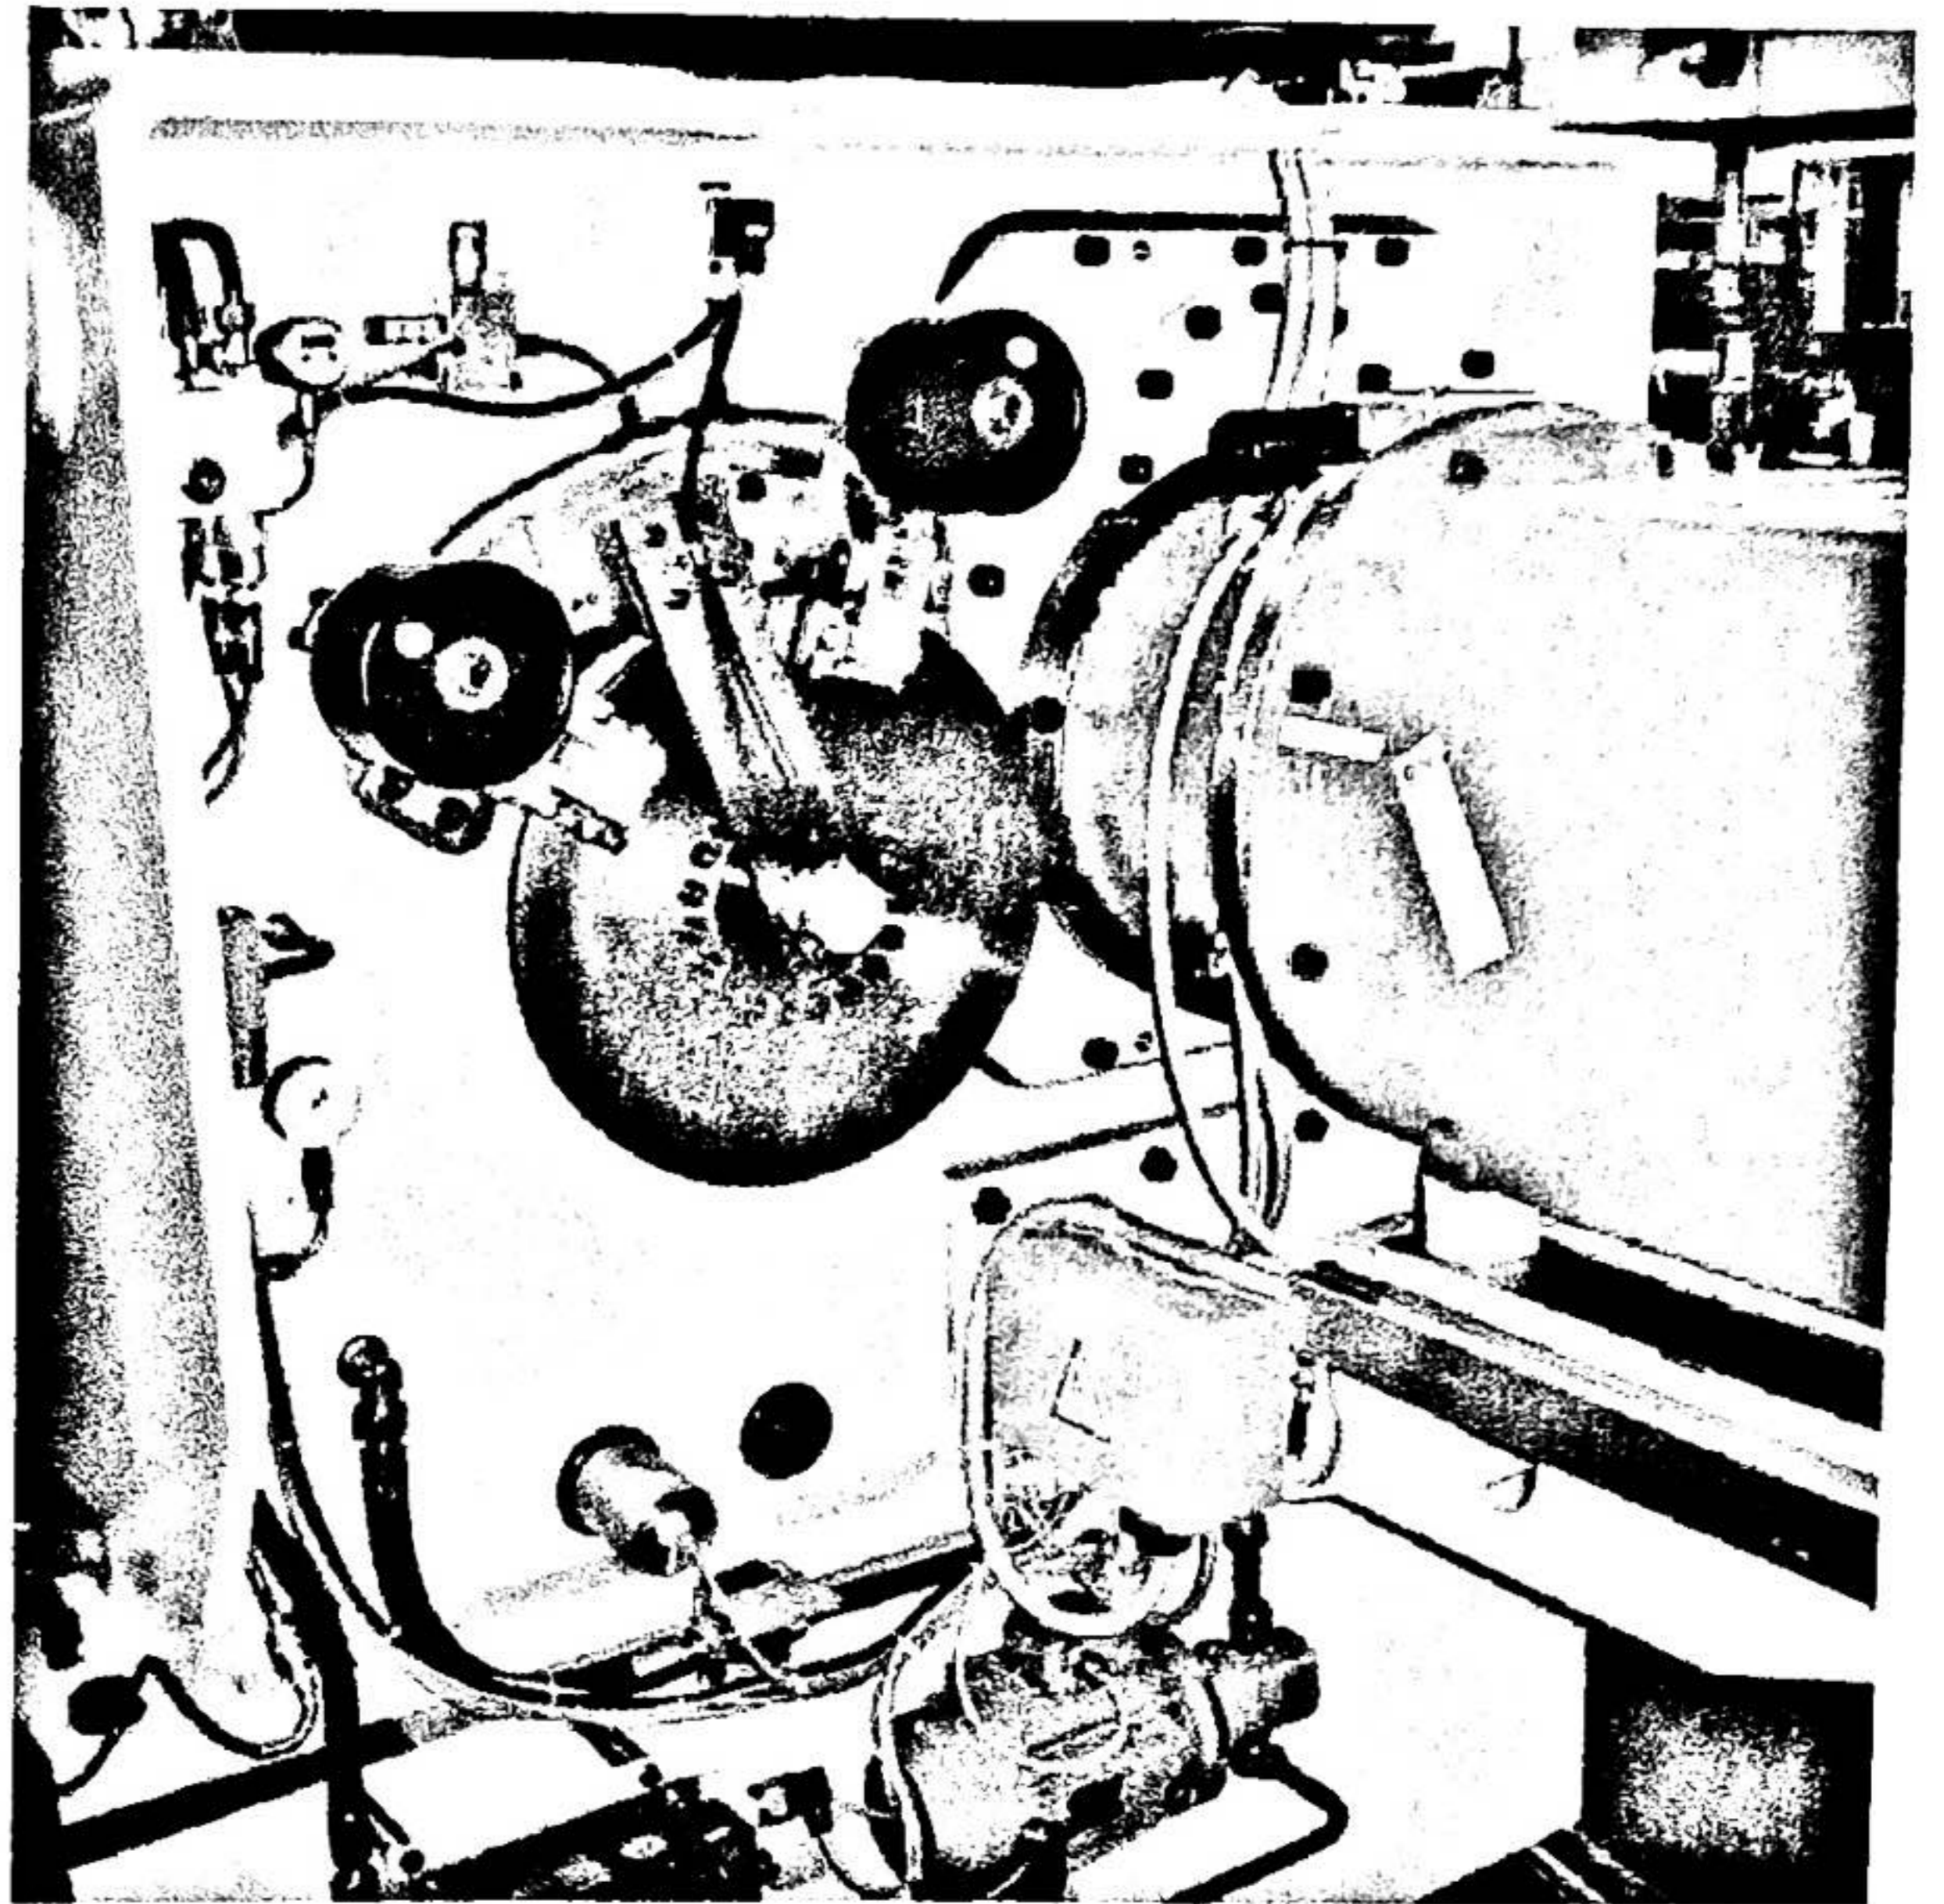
/4: Rückseite Spindelkasten mit Bremse (links), Hauptantrieb (rechts) und Umlaufpumpe (unten)
